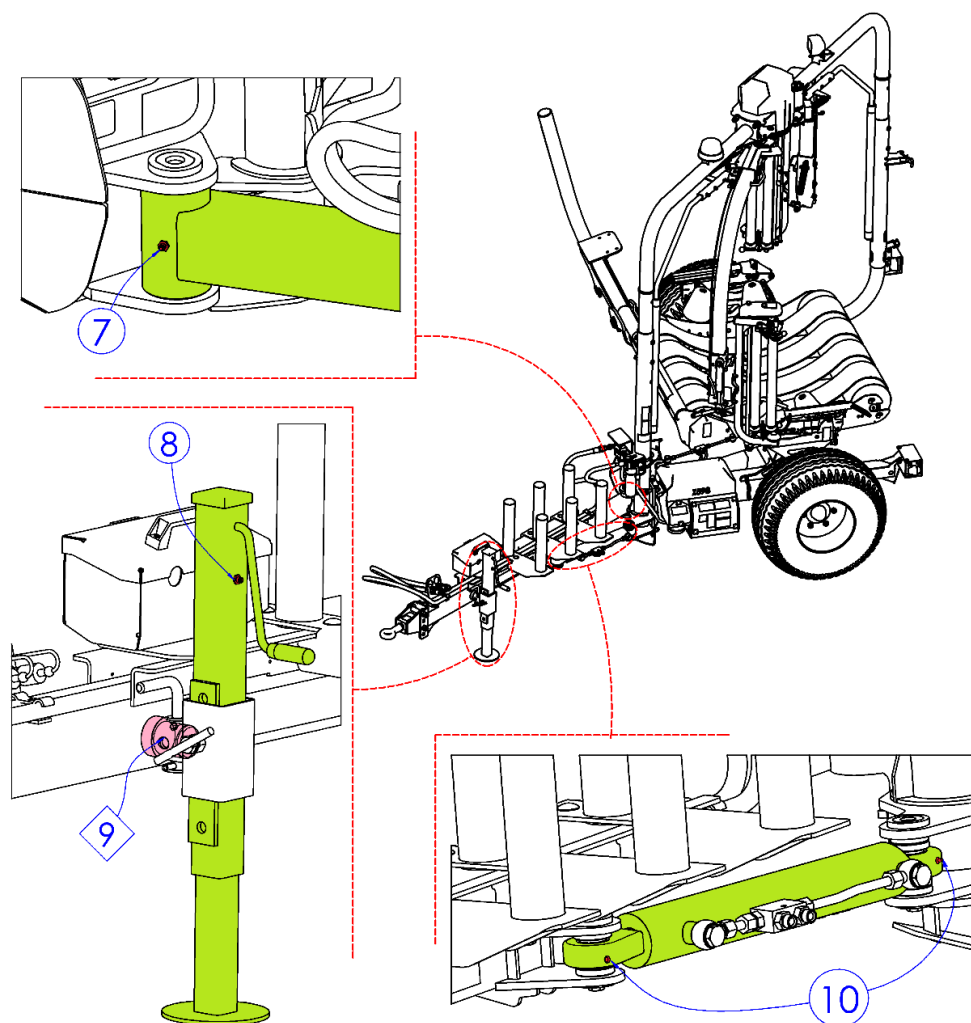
Точки смазки элементов дышла: 7 – смазочные nipples шарнира дышла;
